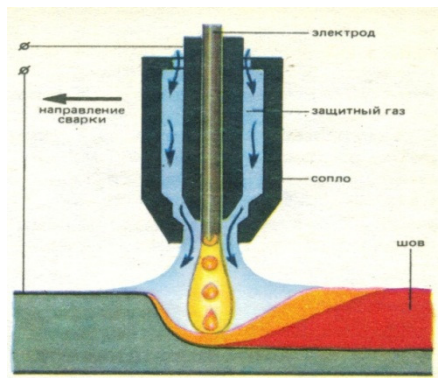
Технологическая схема аргонно-дуговой сварки
